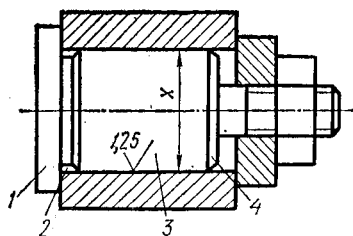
Установка заготовки детали по цилиндрическому отверстию
